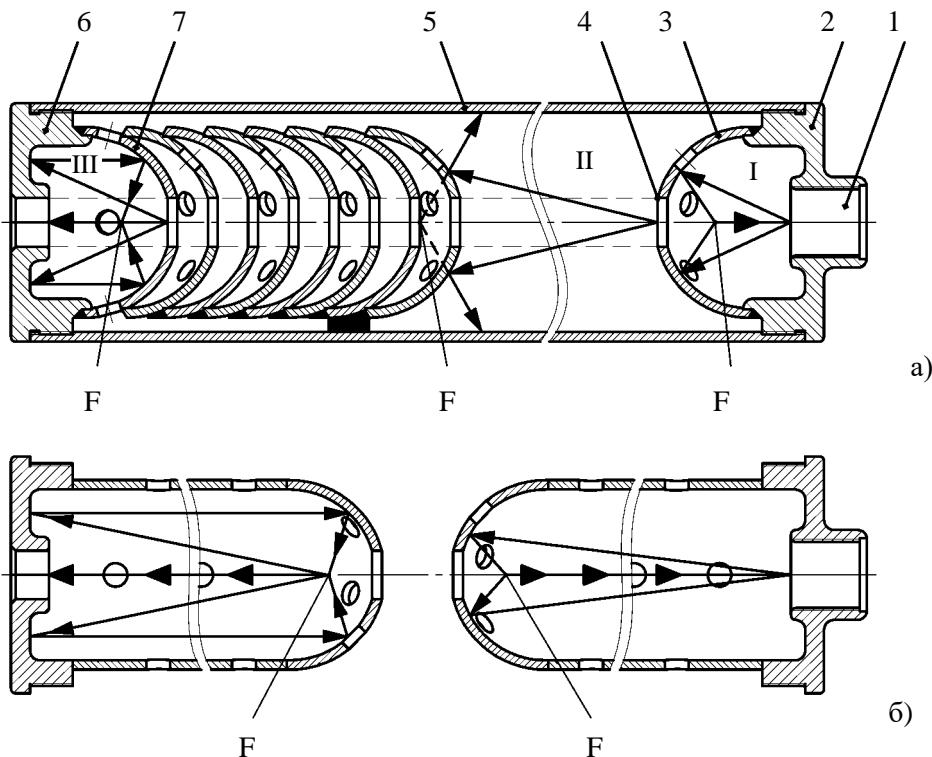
Конструктивная схема глушителя (а) и внутренних элементов рассекателя (б)
